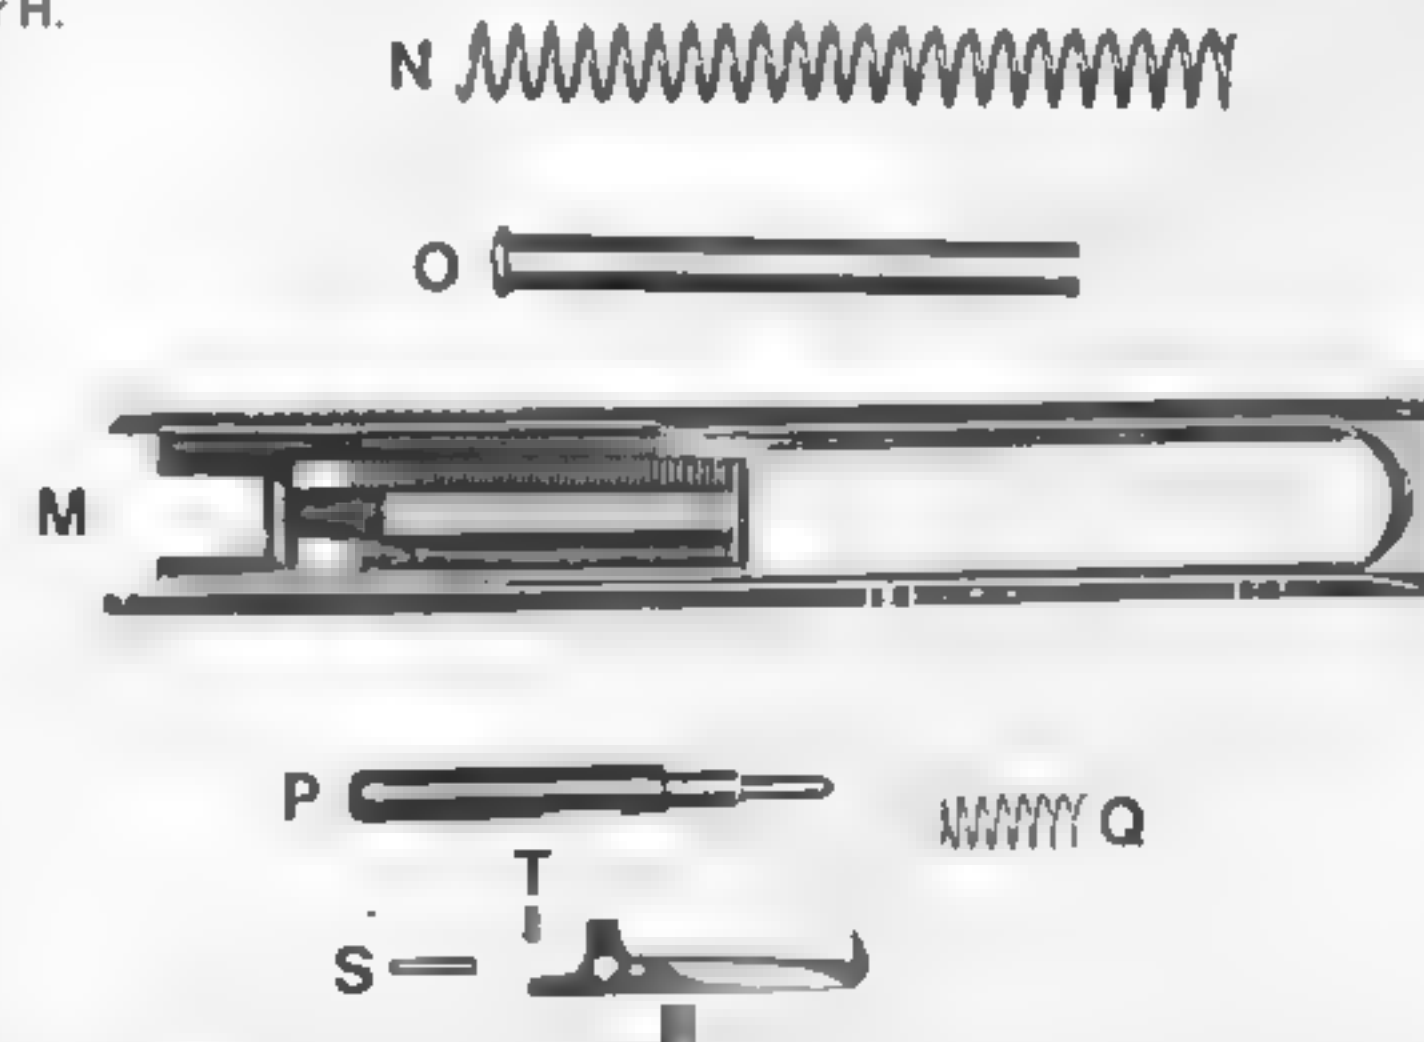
Einzelteile des Verschlusses: M = Verschlussstück, N = Schließfeder, O = Druckbolzen, P = Schlagstift, Q = Schlagstiftfeder, R = Auszieher, S = Auszieherstift, T = Auszieherfeder
